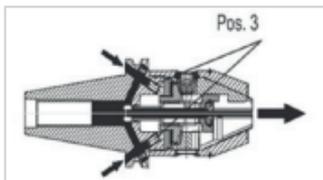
Gewindestifte öffnen Kühlmittelversorgung
